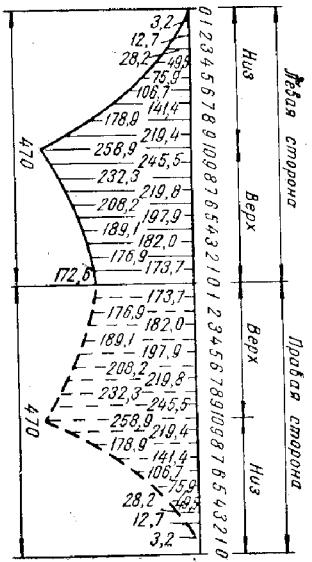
Разметка конца отрезка сварного тройника.
